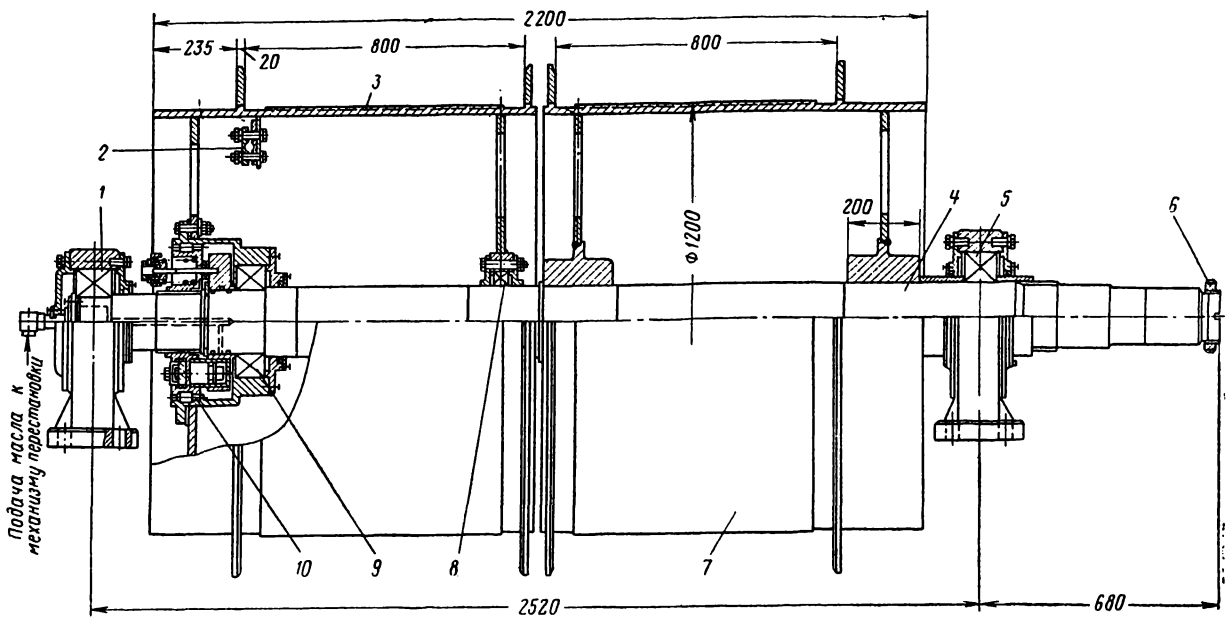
Сборка главного вала машины 2Ц-1,2×0,8:
